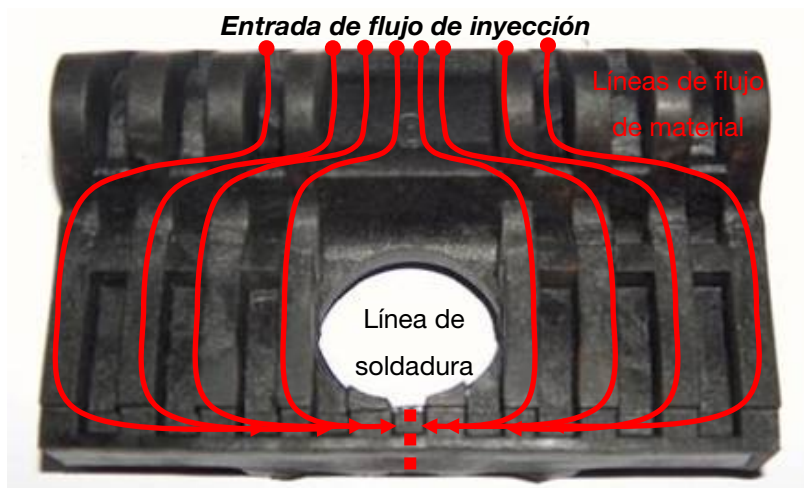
Línea de soldadura de la placa acodada
